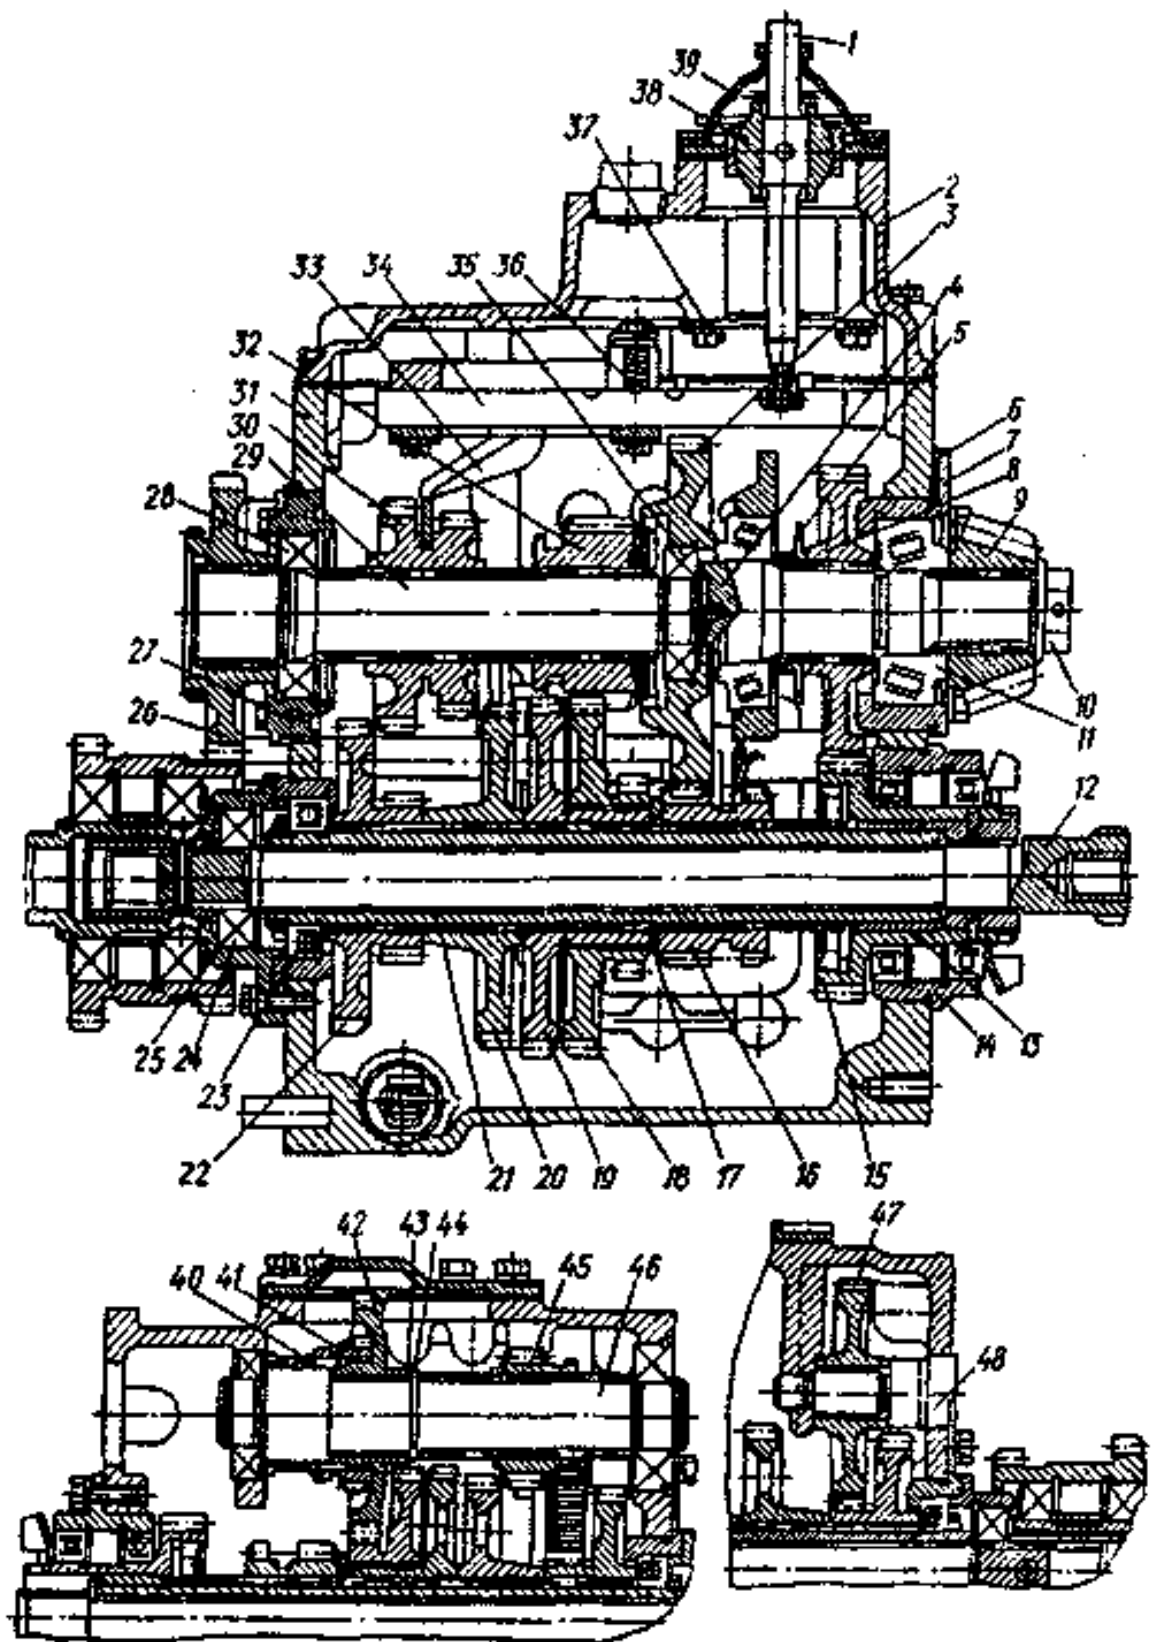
Коробка передач тракторів сімейства ХТЗ з рухомими шестернями:
